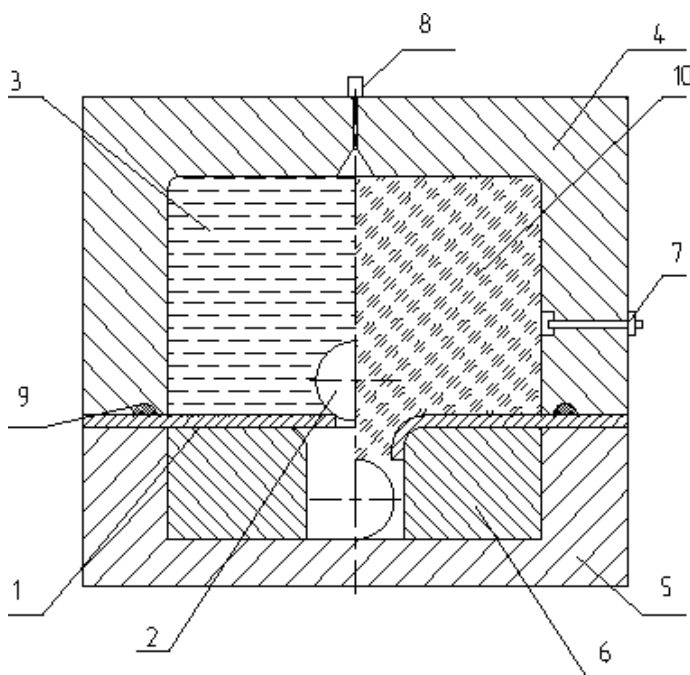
Штамп для отбортовки отверстий в листовой заготовке
